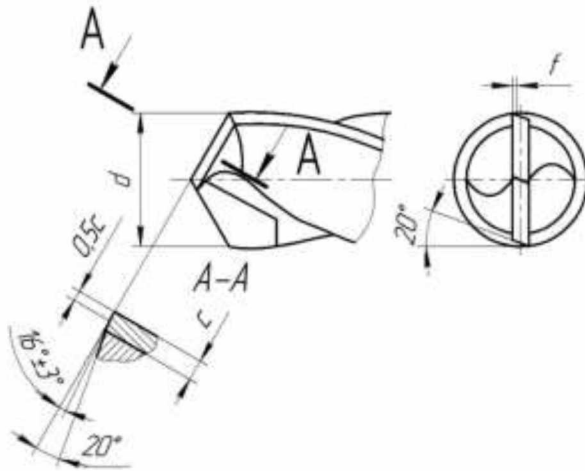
Геометрія робочої частини свердла з напаяними пластинами або коронками із твердого сплаву
